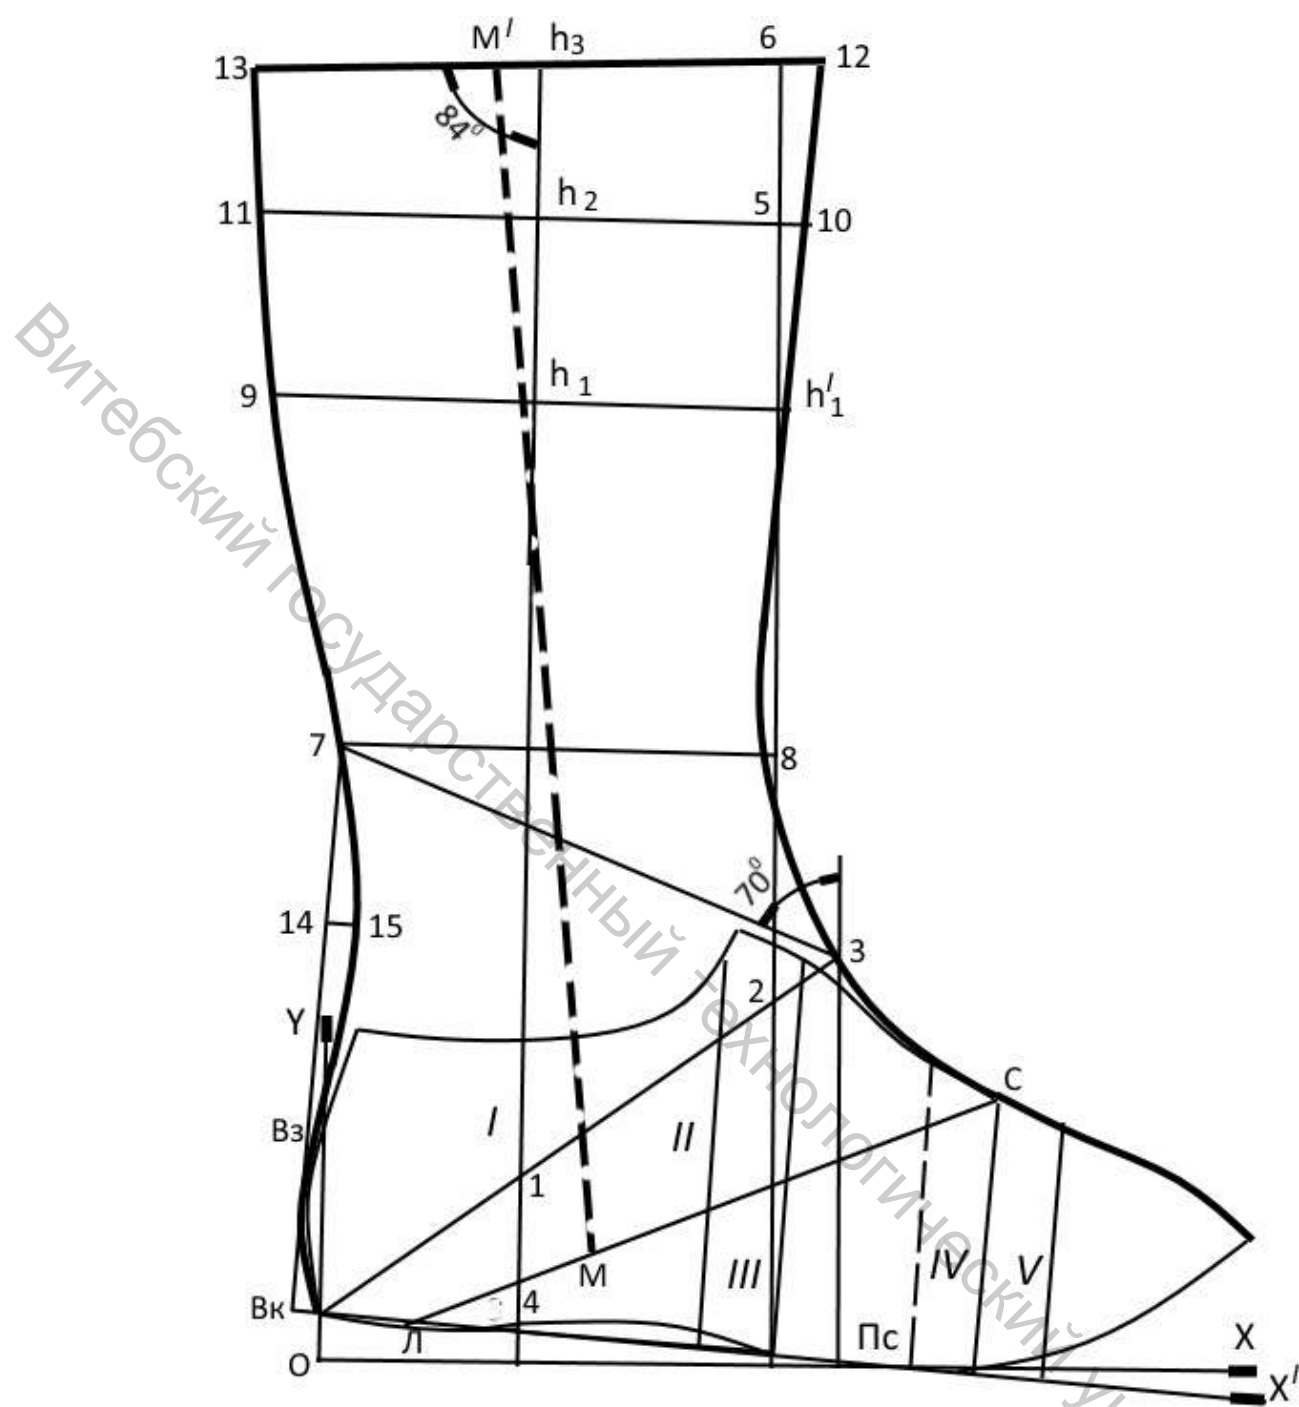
Схема построения чертежа заготовки высоких женских сапожек
